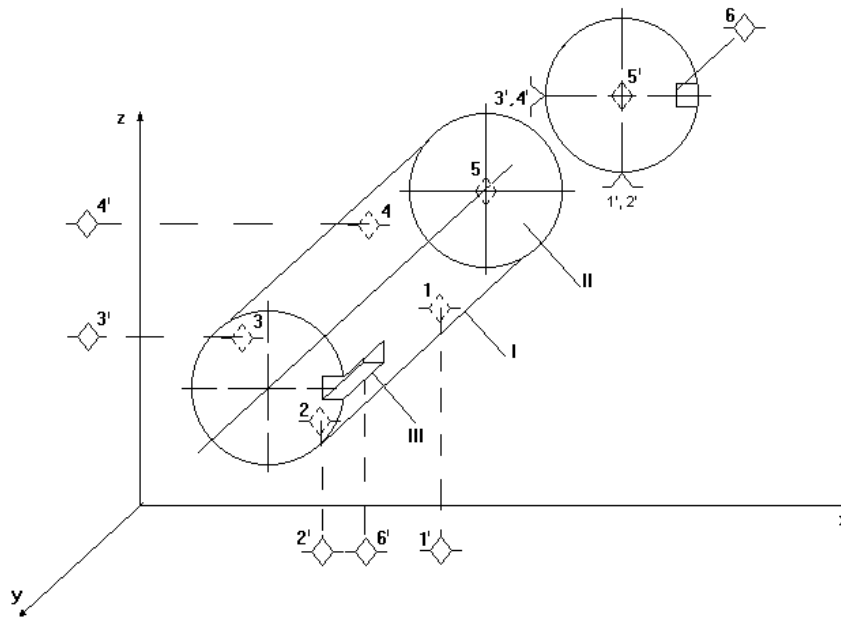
Приклад розташування опорних точок на циліндричній заготовці з комплектом баз IV, III, III' (опорна база III' позбавляє заготовку можливості обертання навколо осі Y)
